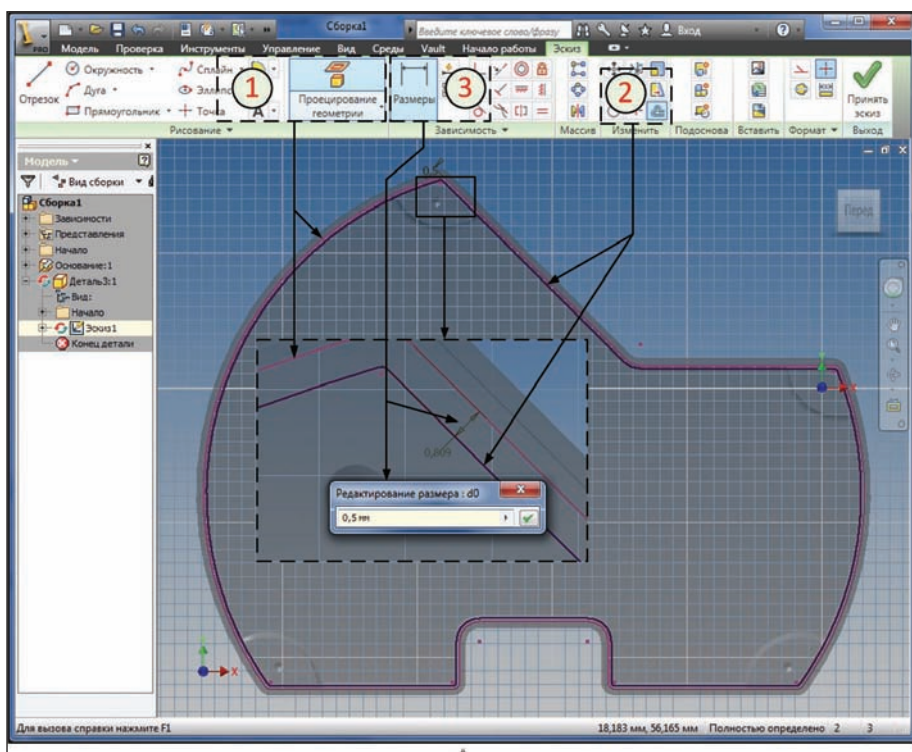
Формирование контура "электронной заготовки" печатной платы
